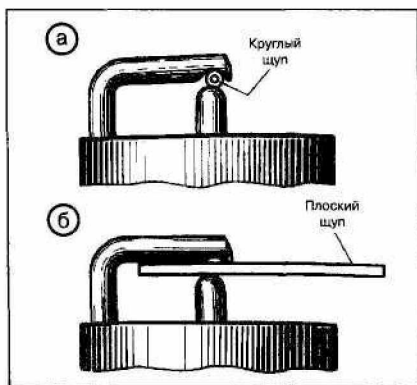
Проверка зазоров между электродами свечи: а — верно; б — неверно
